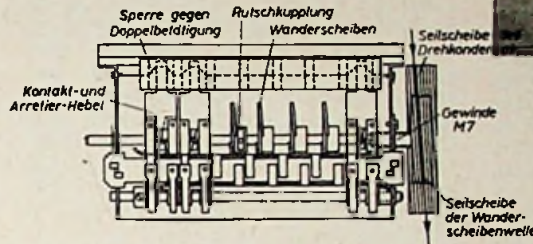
Die praktische Ausführung des „mechanischen Gedächtnisses“
